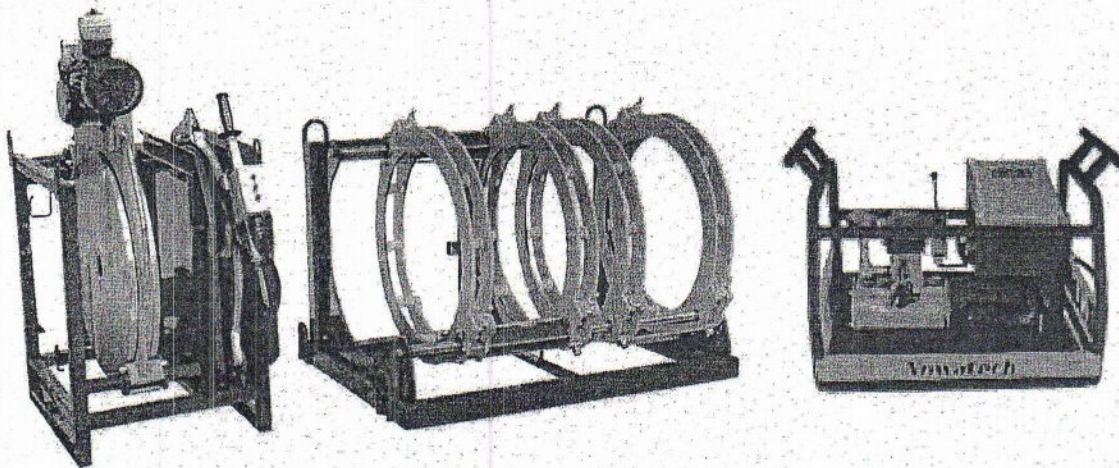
Общий вид сварочного аппарата типа ZHCB 630
